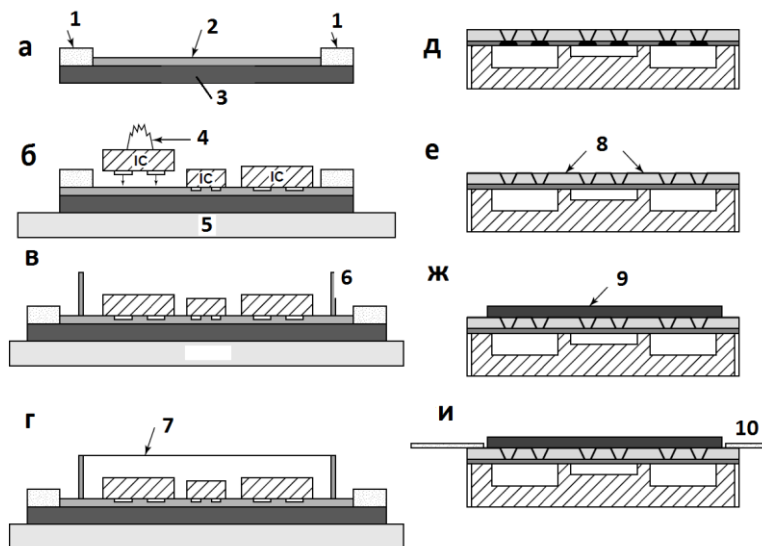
Техпроцесс изготовления ГИС в пластиковом корпусе:
